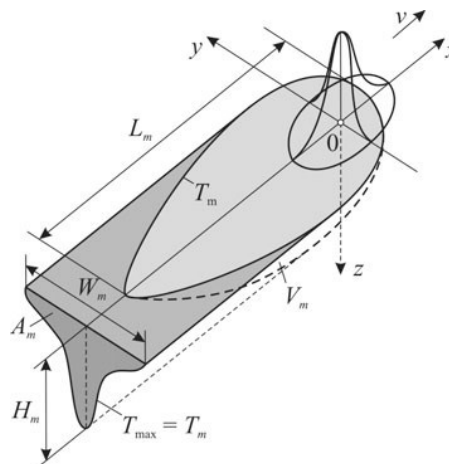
Parámetros geométricos del baño de soldadura. [38]
